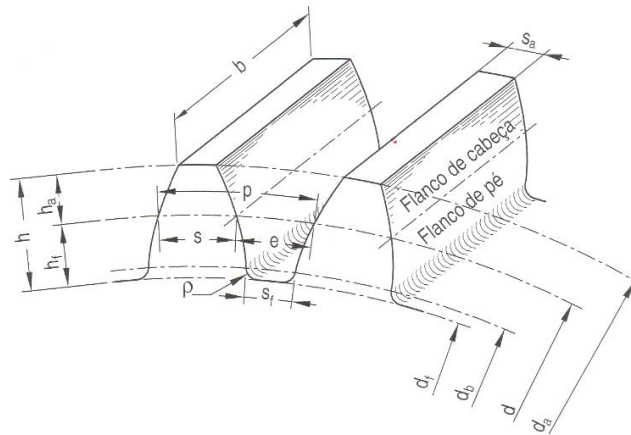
Nomenclatura dos dentes de uma engrenagem de dentes retos [5]
